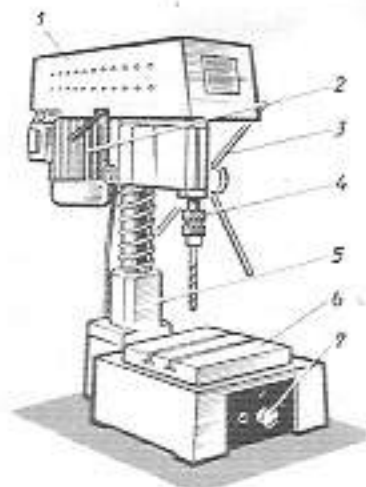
Настольный сверлильный станок: 1 — кожух; 2 — электродвигатель; 3 — рукоятка; 4 — патрон; 5 — станина; 6 — стол; 7 — пульт с кнопками.
